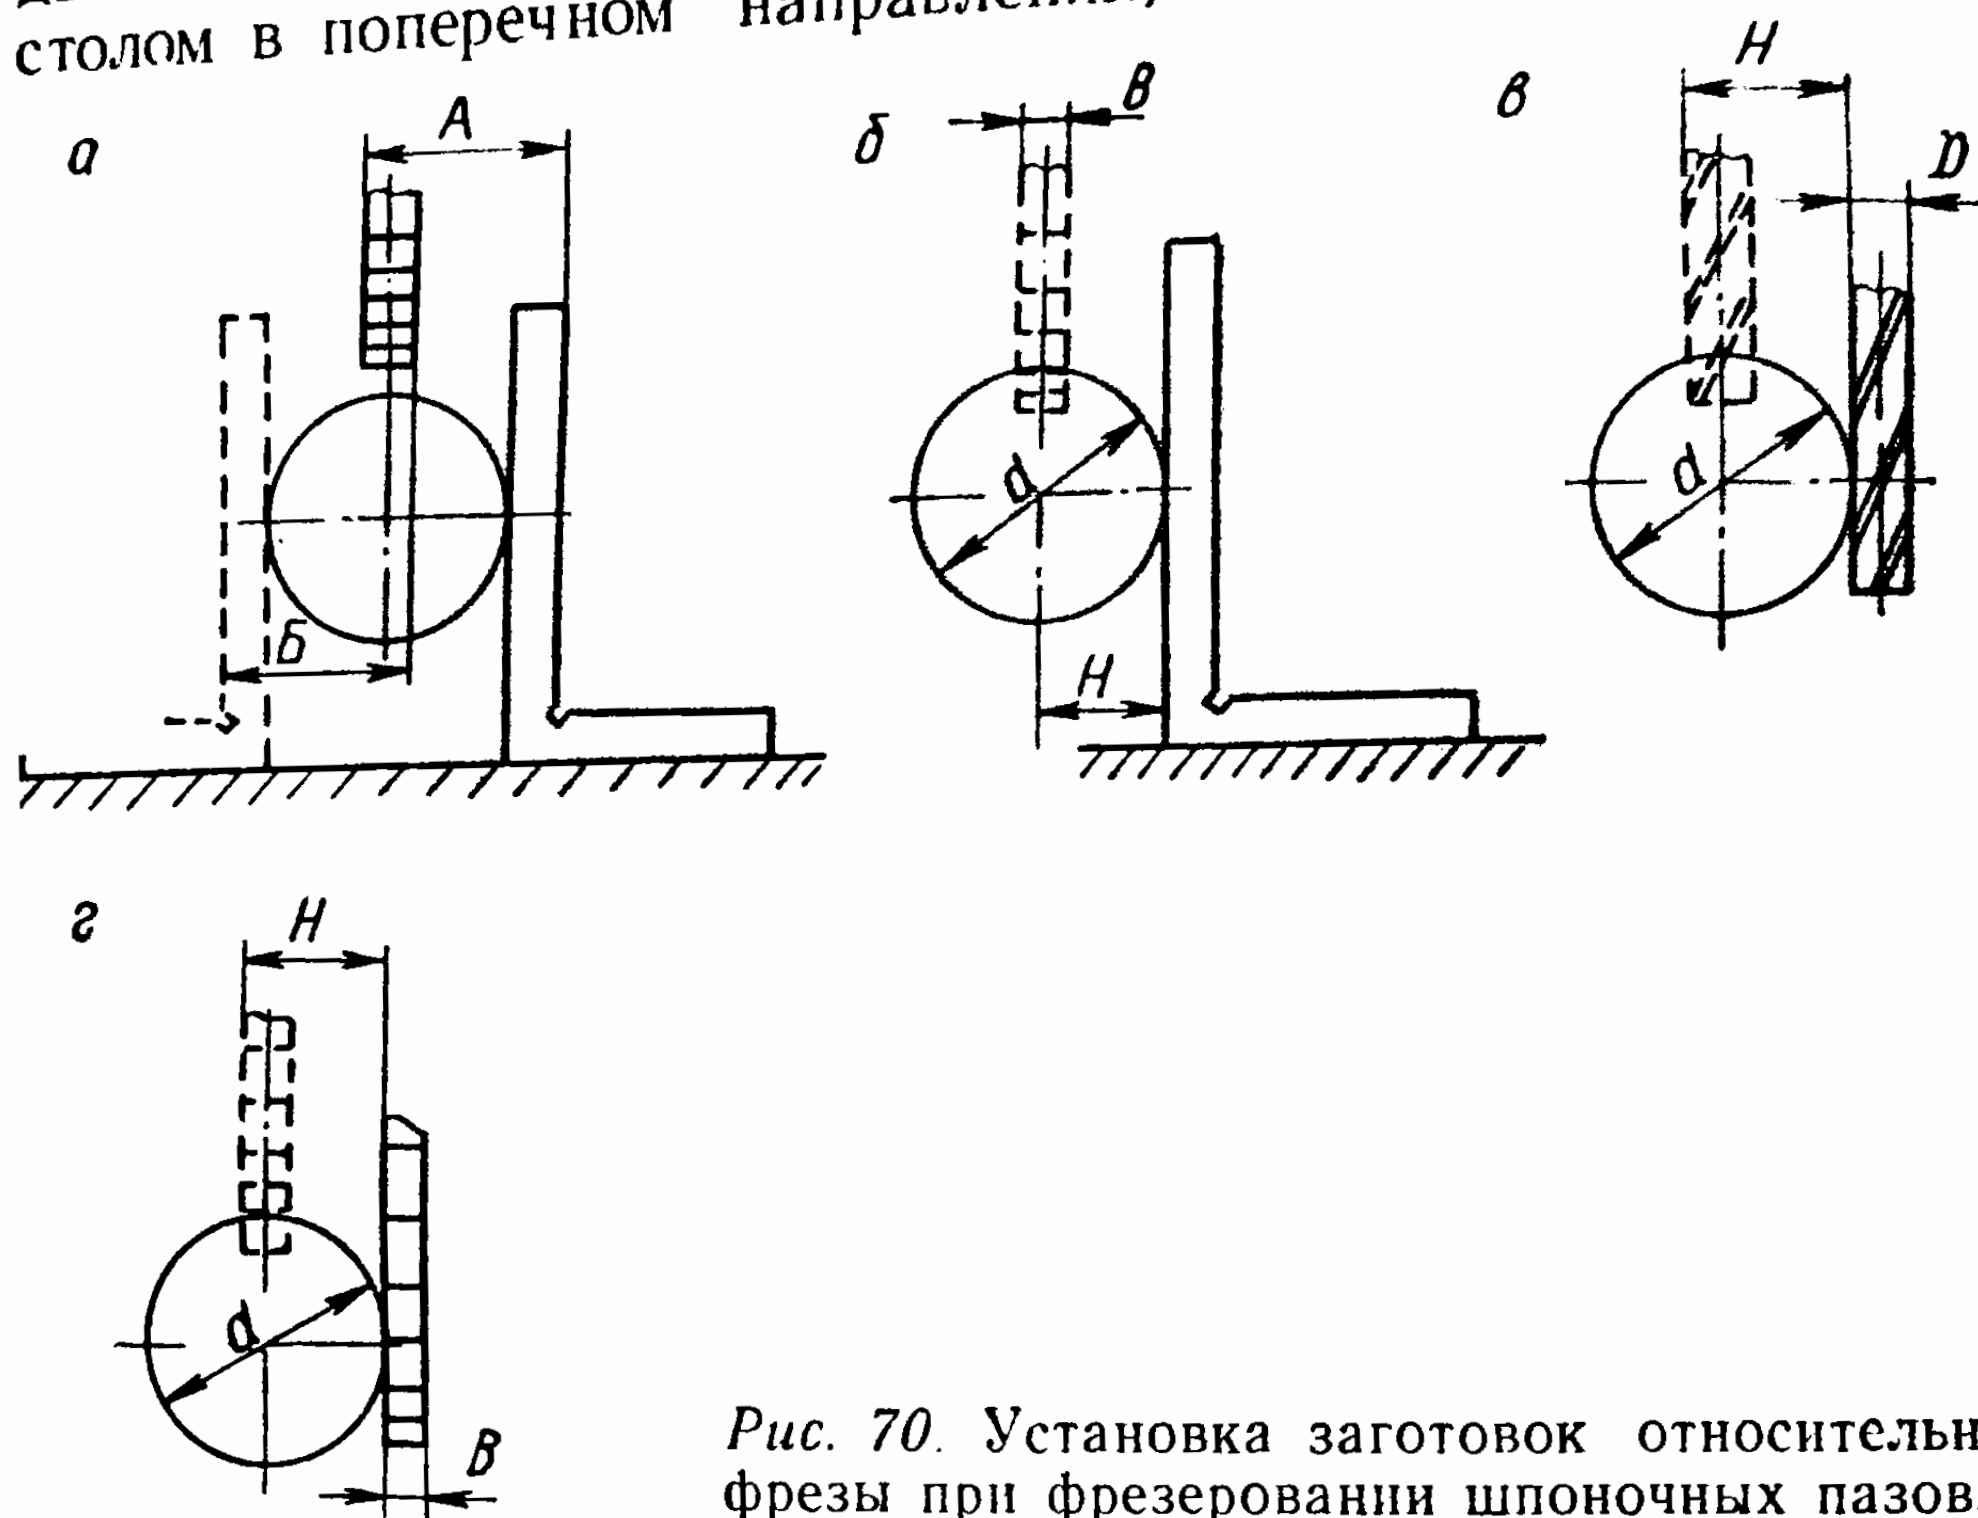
Установка заготовок относительно фрезы при фрезеровании шпоночных пазов.
